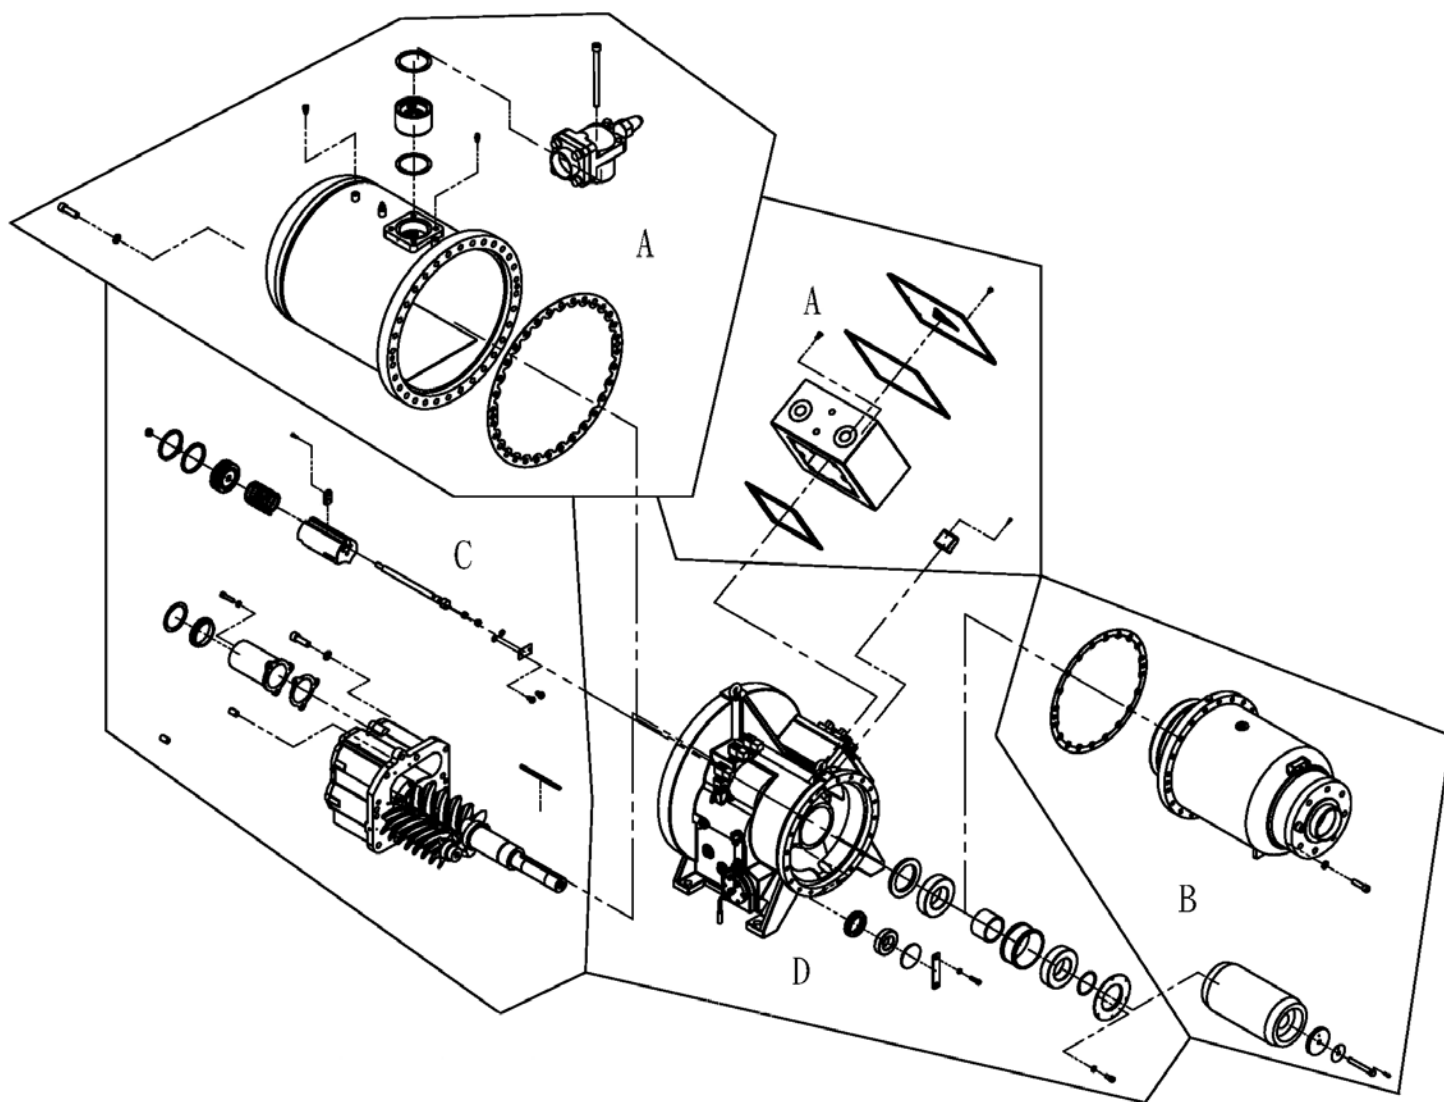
SR-8 (H) ~SR-8 (H) 分解說明/ Disassembly illustration
